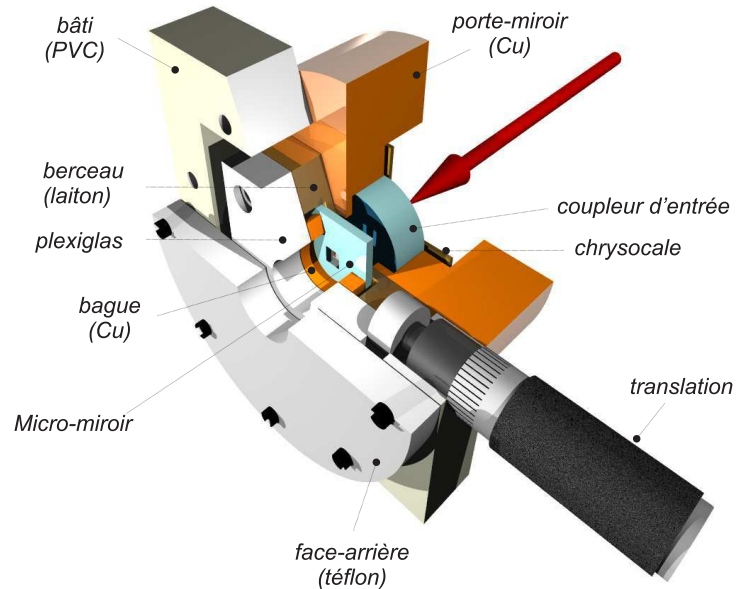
Vue en coupe de la deuxième version de la cavité de mesure.
